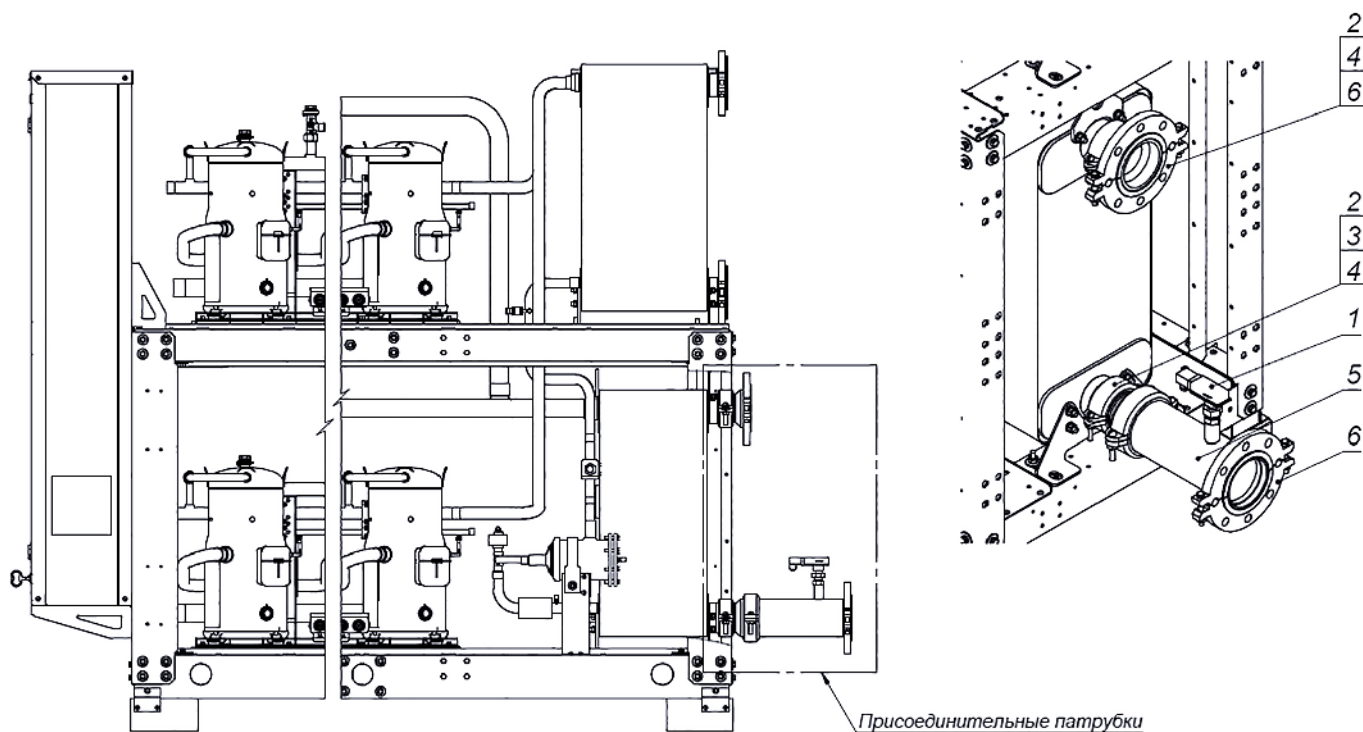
Схема сборки присоединительных патрубков гидравлического контура чиллеров.
